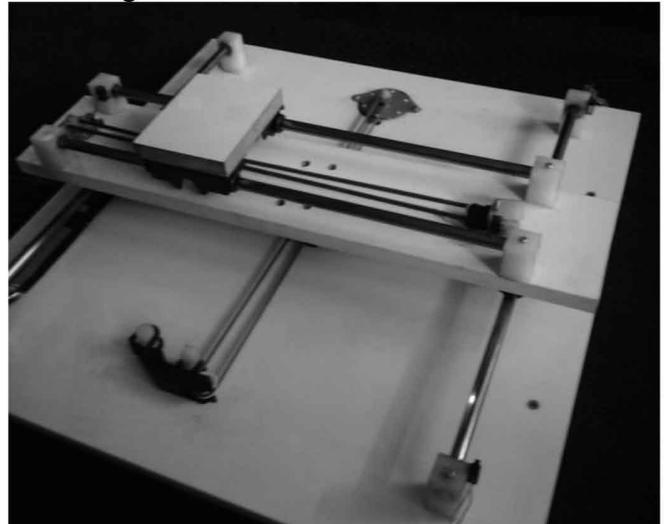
Mesa fixa com motor, mancal, eixo e correia instalada
